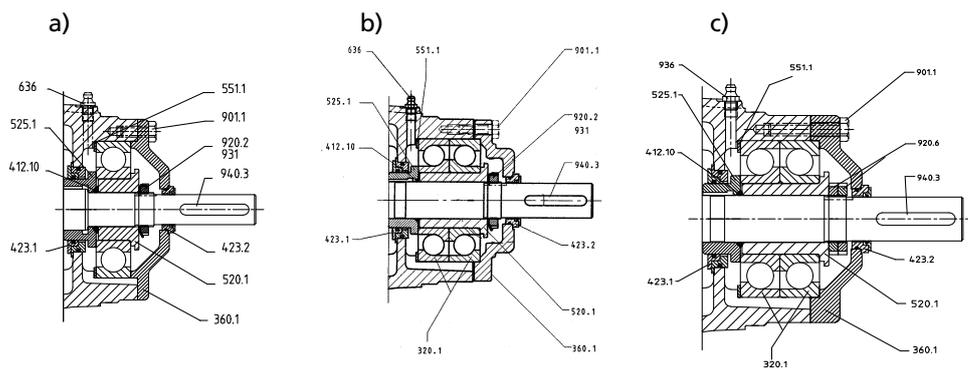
Консистентная смазка с лабиринтным уплотнением: а) типоразмер 32 и б) типоразмер 50-65 и с) типоразмер 100-200
